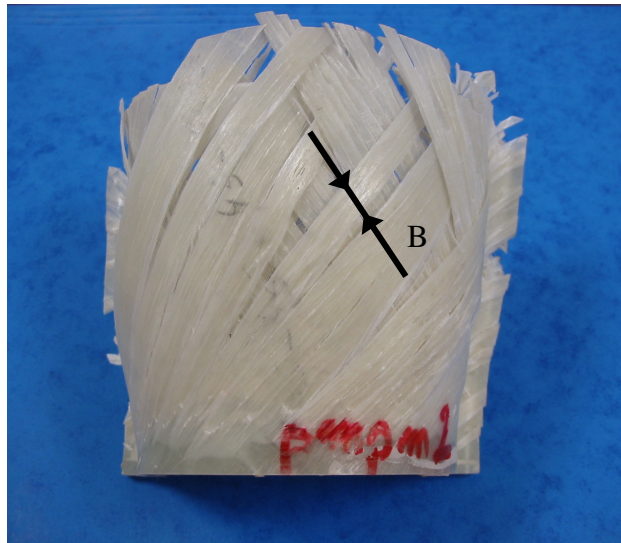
Bandes de plis formées par la fissuration intralaminare.
